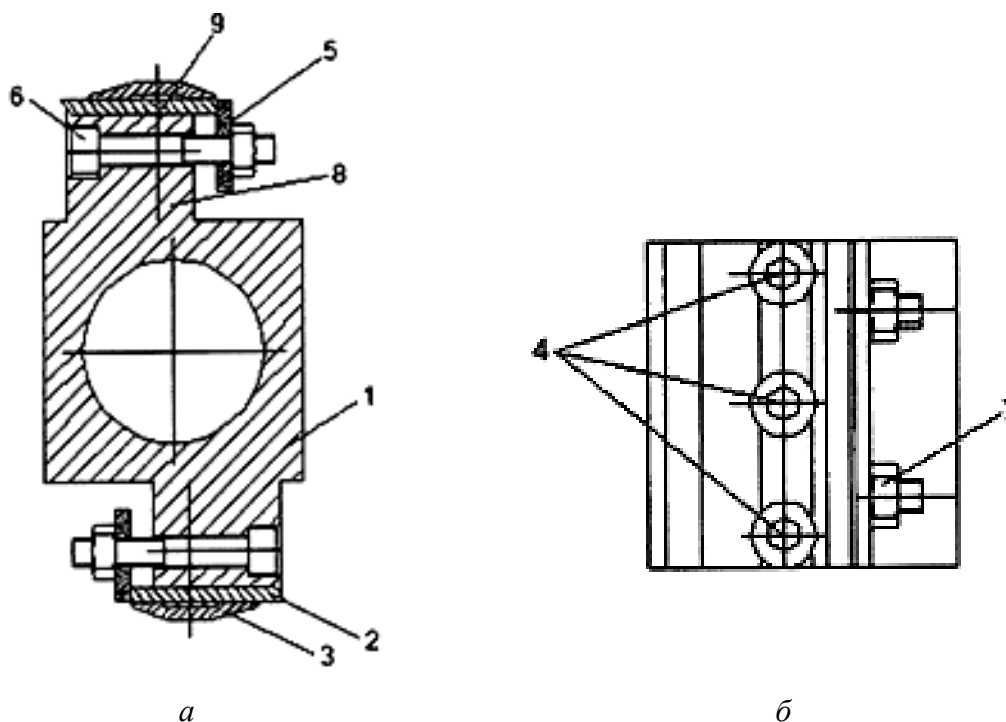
Сборная фреза деревообрабатывающего станка по патенту России № 125121:
